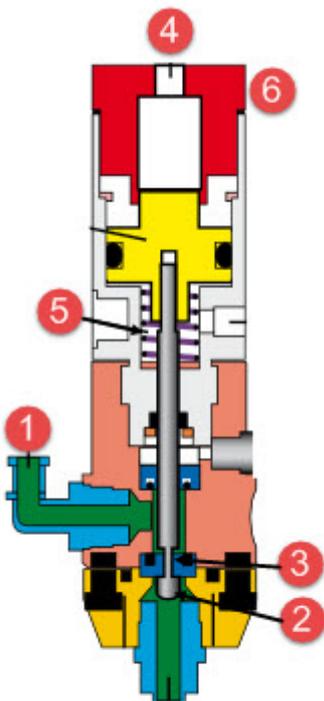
Prinzipskizze Kolbenventil (Quelle: Fa. Vieweg)
